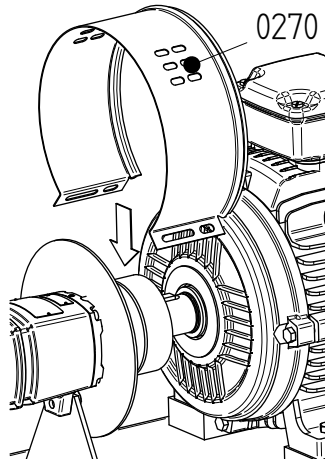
Montage der Schutzhaube auf der Motorseite.
